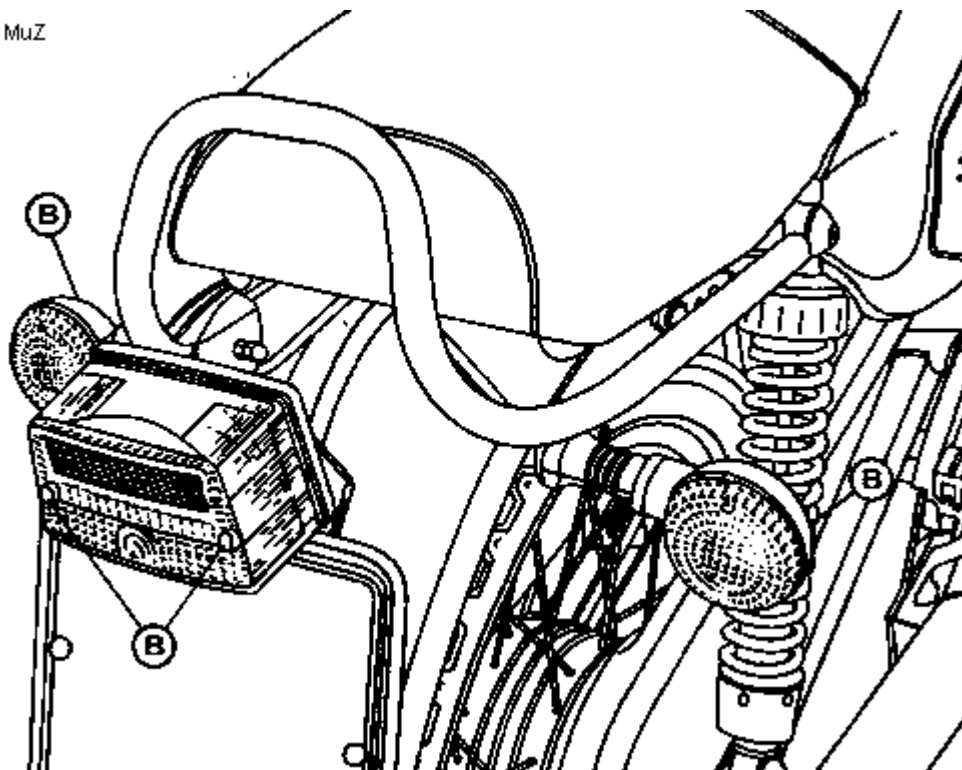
Rückleuchte und Blinkleuchten (B) Befestigungsschrauben
